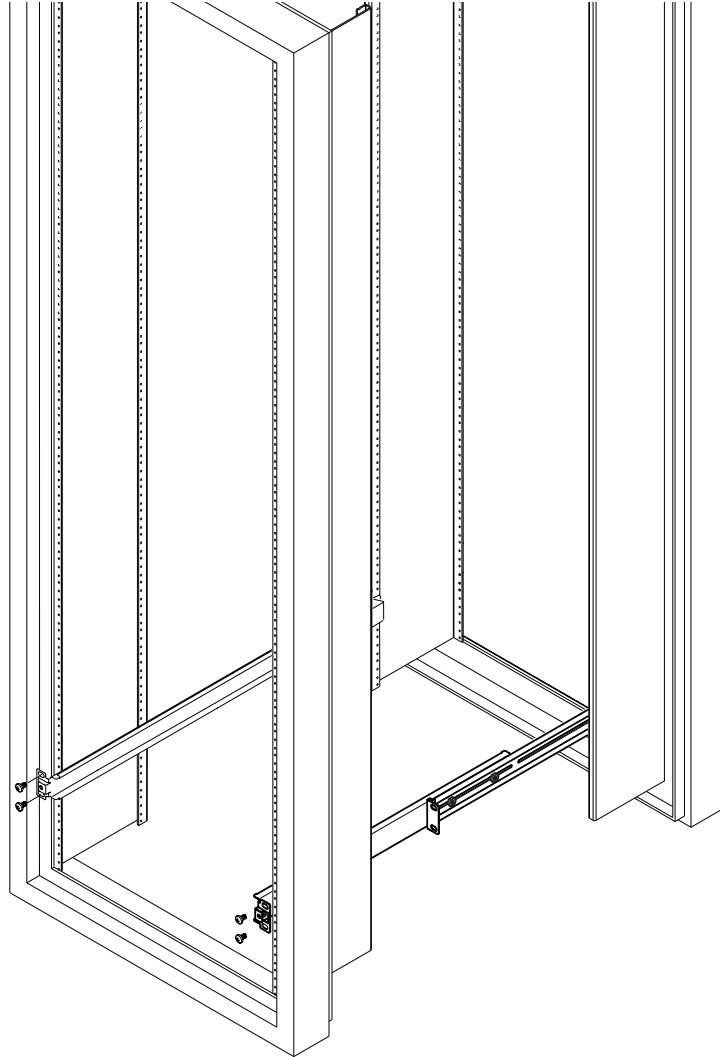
Fixation des supports guidés sur un châssis à expansion Sun StorEdge de 72 pouces - Vue avant (panneaux latéraux retirés à des fins de clarté)
